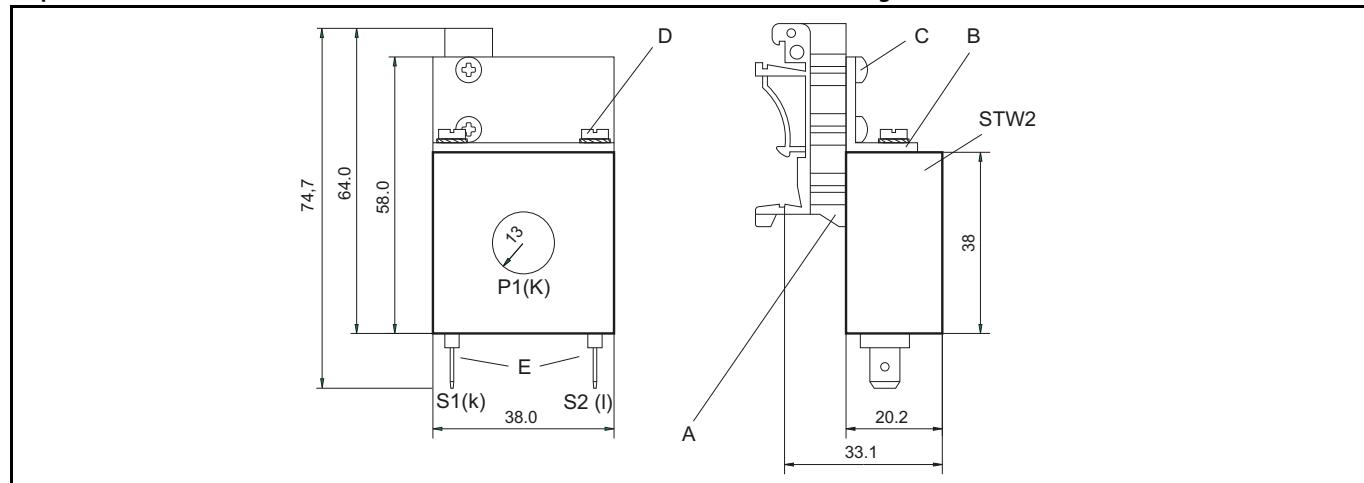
Variante de montaje 1 (todas las dimensiones en mm)
